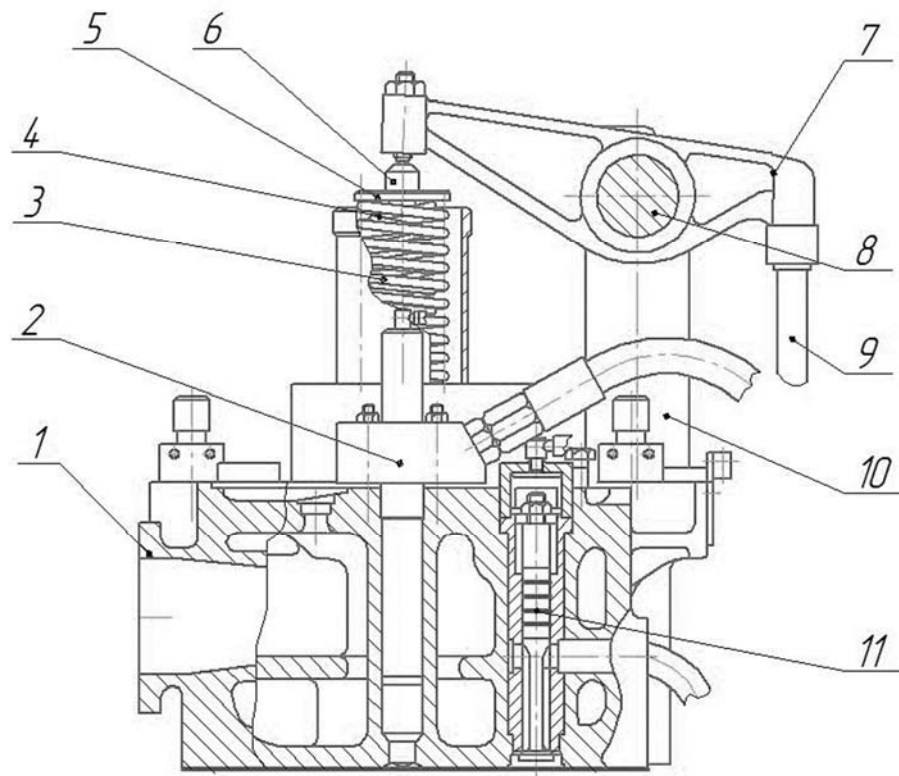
Кришка блоку циліндрів: 1 – корпус головки; 2 – форсунка; 3 – зовнішня пружина клапана; 4 – внутрішня пружина клапану; 5 – верхня тарілка клапану; 6 – клапан; 7 - коромисло; 8 – вісь коромисел; 9 – штанга; 10 – опорна стійка; 11 – повітряний клапан
